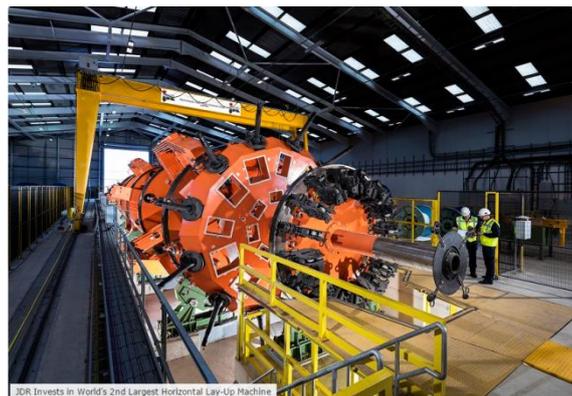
JDR's Horizontal Lay-up Machine(HLM)
